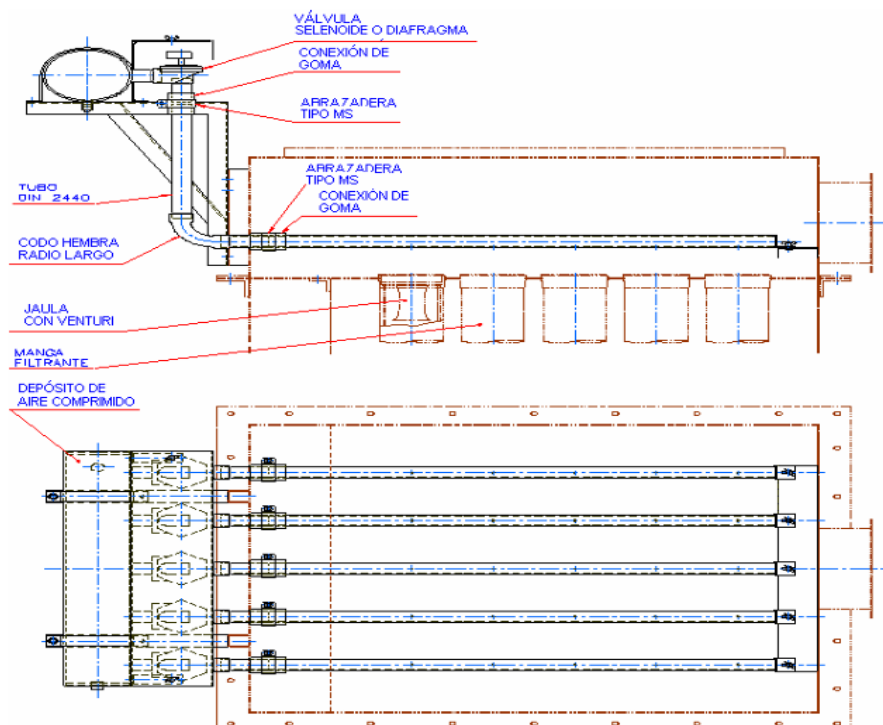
Vista general en Planta del Sistema de inyección de Aire a las Magnas
